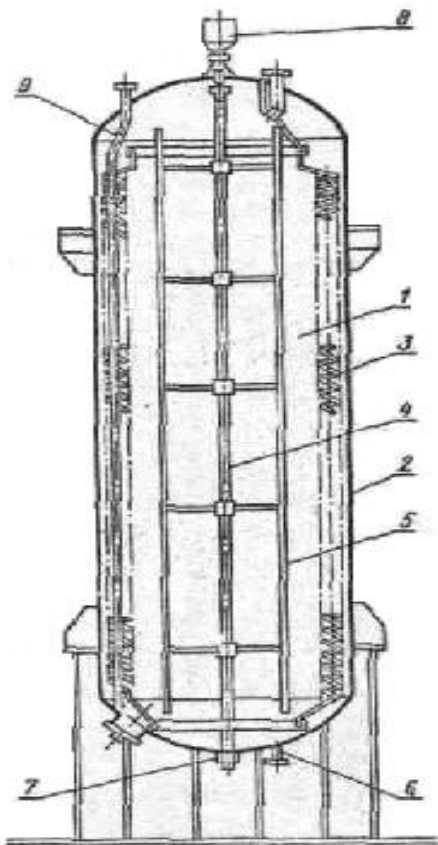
Устройство автоклава: 1 — корпус; 2 — теплоизолированная стенка; 3 — змеевик; 4 — вал; 5 — рамная мешалка; 6 — штуцервывода конденсата; 7 — поднятник мешалки; 8 — привод мешалки; 9 — переточная труба
